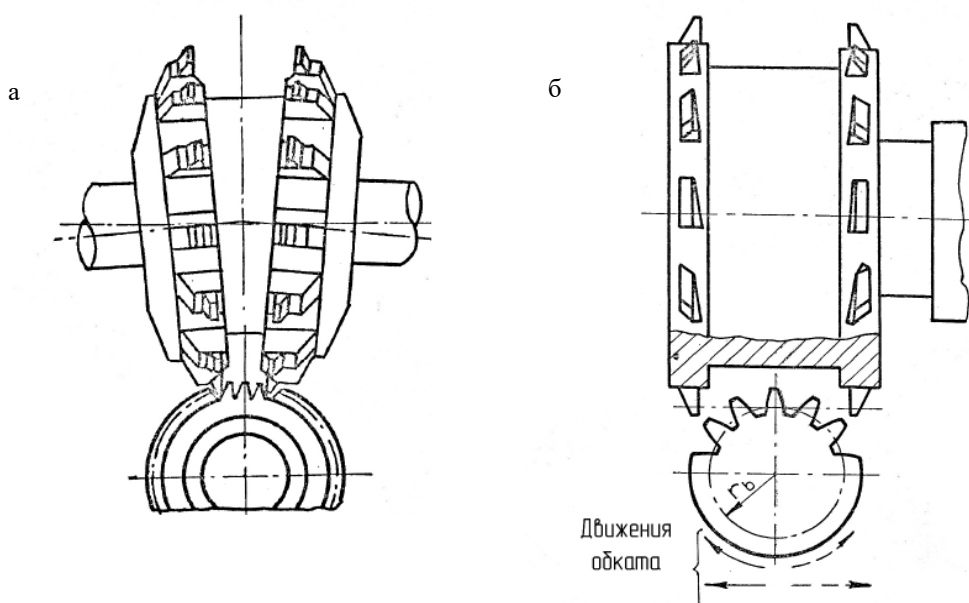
Зубообработка резцовыми головками: а – с клиновой шайбой; б – с нулевым углом профиля [6]
